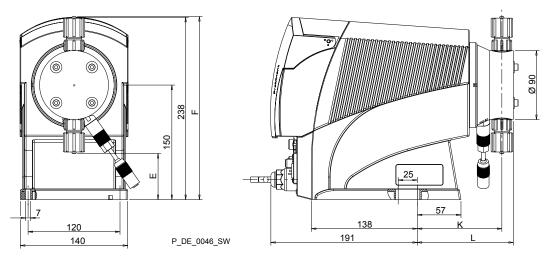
Hoja de dimensiones del tipo delta® sin válvula de aireación, versión de material NP - Dimensiones en mm
